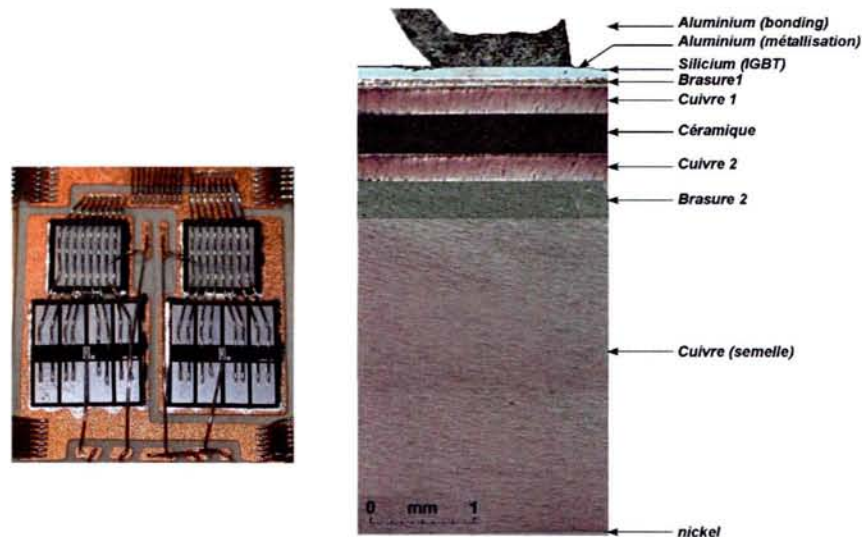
Fils de bonding sur puces silicium et vue en coupe d'un module IGBT 600V-200A
